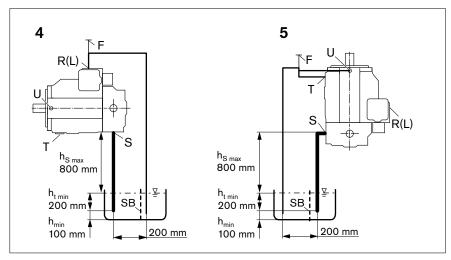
Montaje sobre el tanque con posición de montaje horizontal 4 y vertical 5
